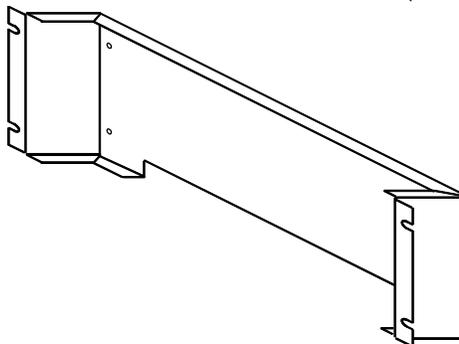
Soporte adaptador para montaje encajado IC693ACC313
